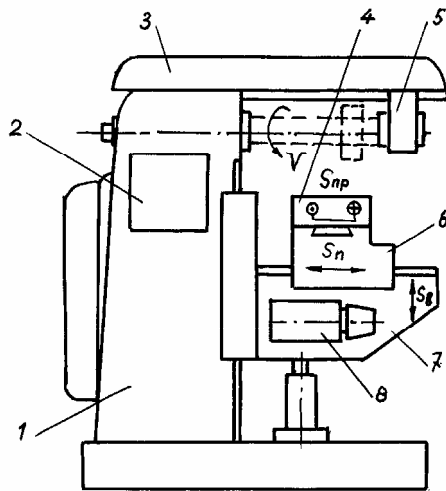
Компонновка основных узлов горизонтально-фрезерного станка:
